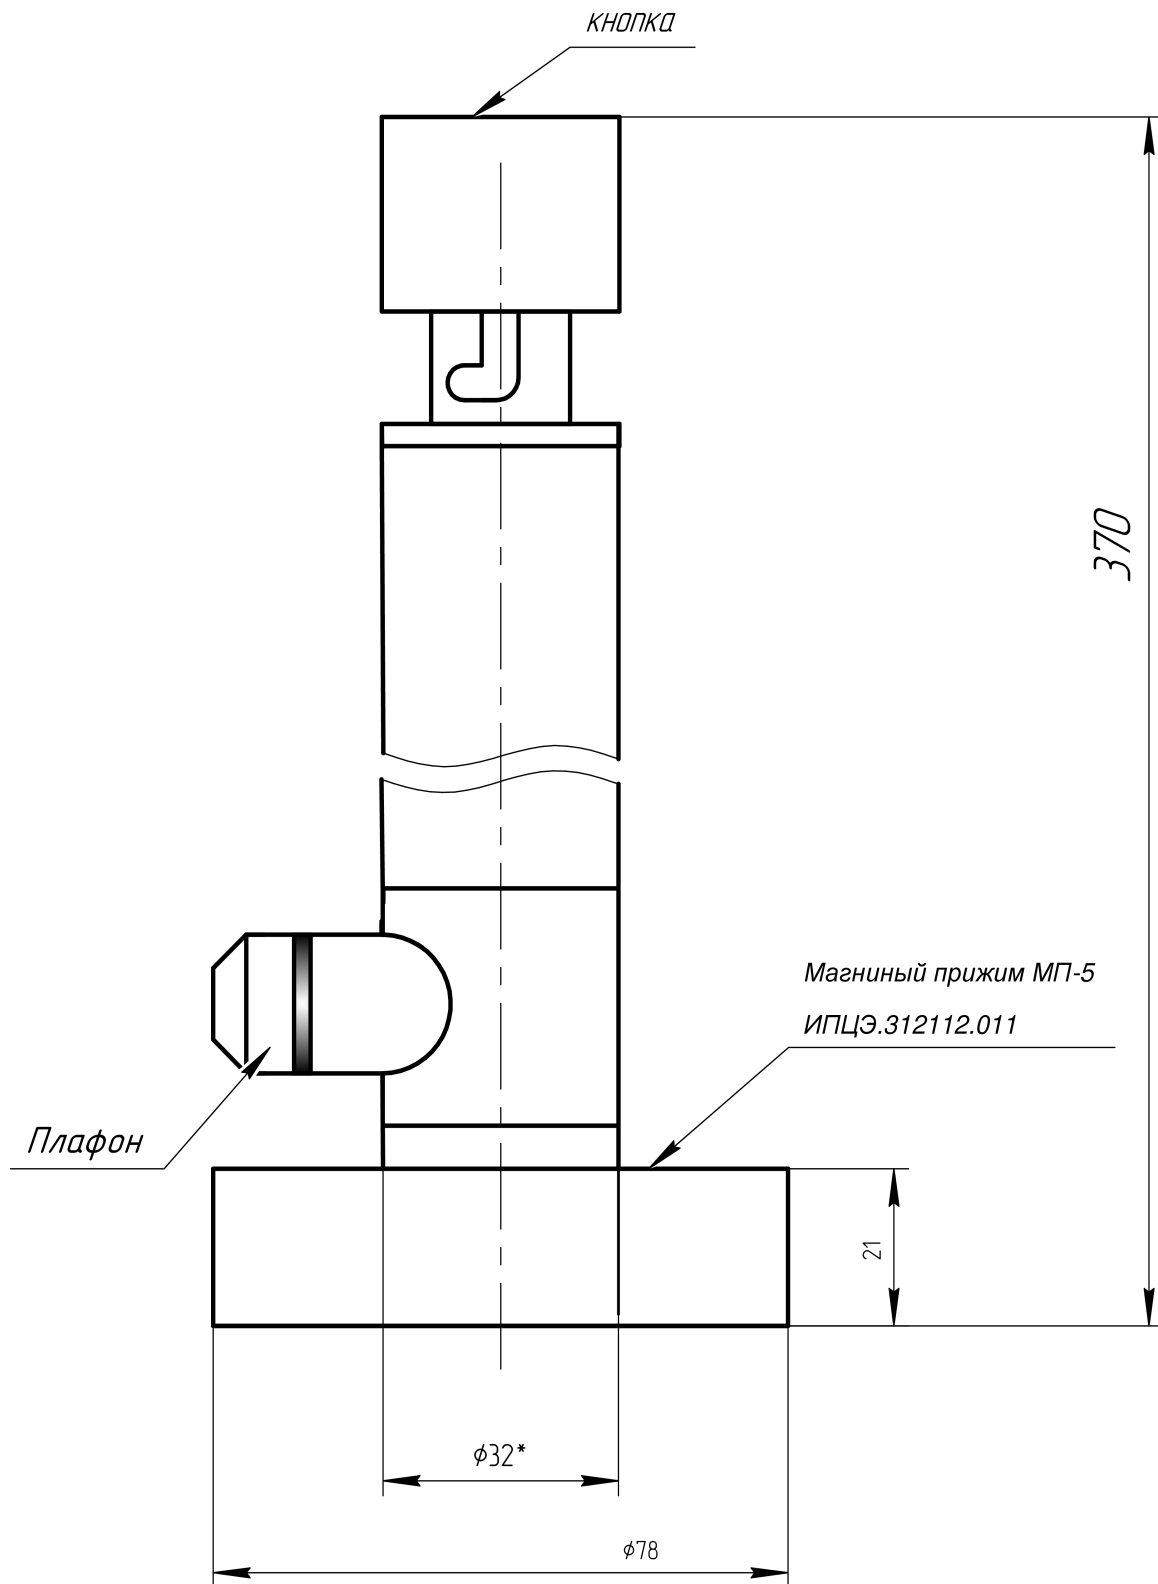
Имитатор ИРС-1. Габаритный чертёж
